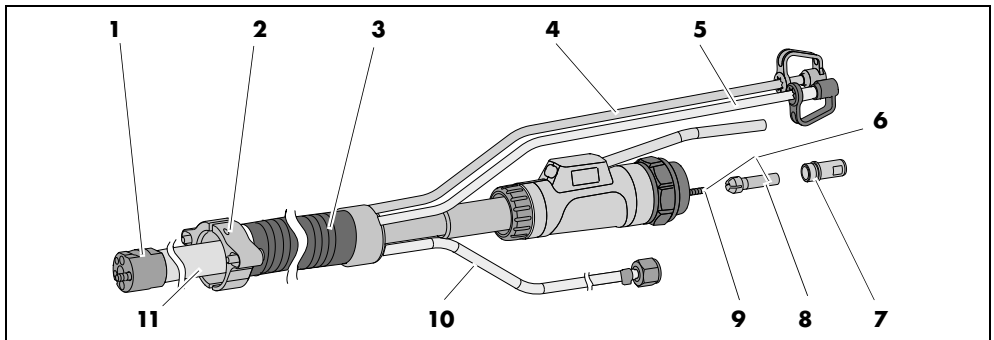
Ersatzteilliste Schlauchpaket / Hose assembly ABIROB® W
